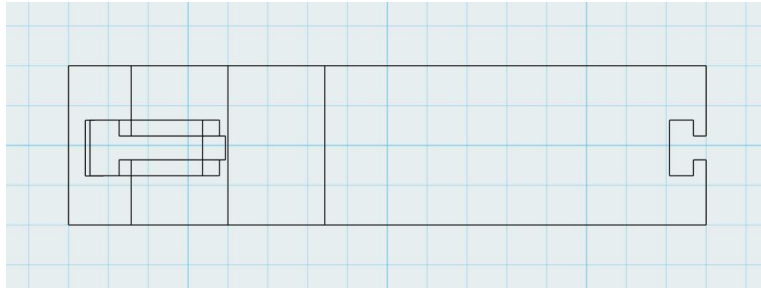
Technische Zeichnung des ersten Prototyps von oben (1 Häuschen = 5mm)
